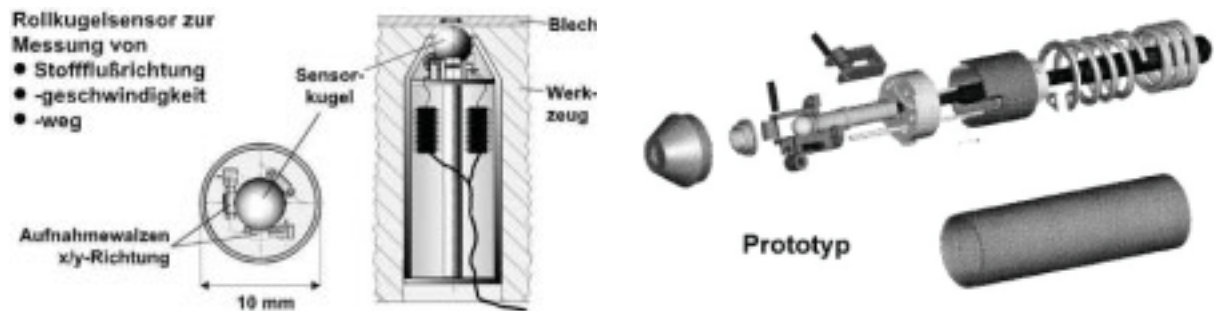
Aufbau des Rollkugelsensors [Gri99]
